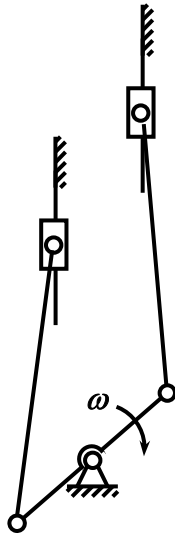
Механизм двухступенчатого двухцилиндрового воздушного компрессора
